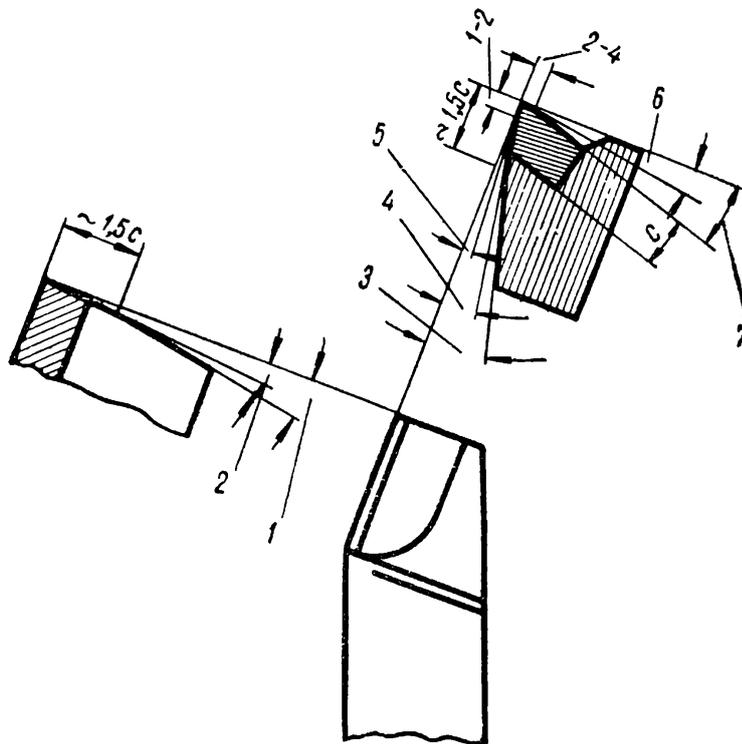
Двойная и тройная заточка резца, оснащенного пластинкой твердого сплава:
